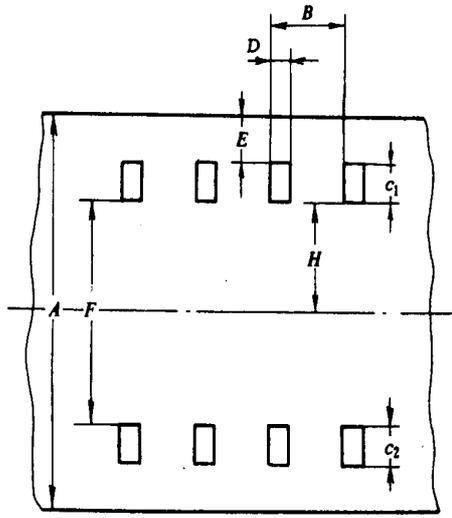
载带自动焊接封装部位尺寸图
